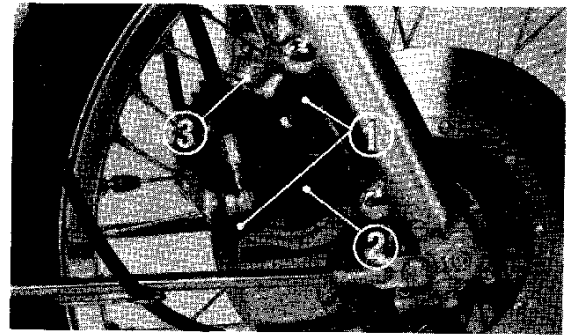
(1) 8 mm-Innensechskantschrauben
